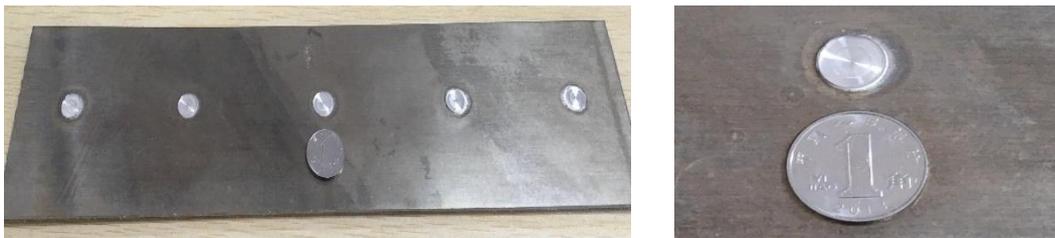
焊接效果(材质 Al 厚度 2mm)
